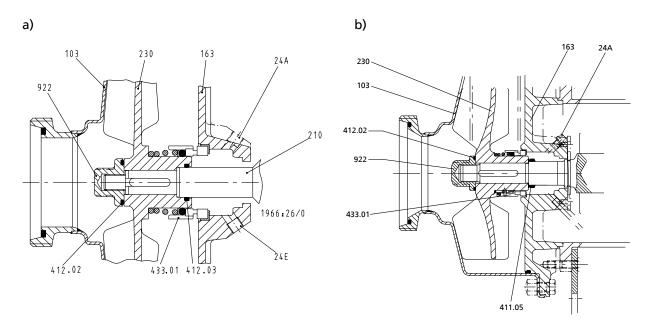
Einzelgleitringdichtung a) mit O-Ring (Baugrößengruppe I) b) mit V-Ring (Baugrößengruppe II)
